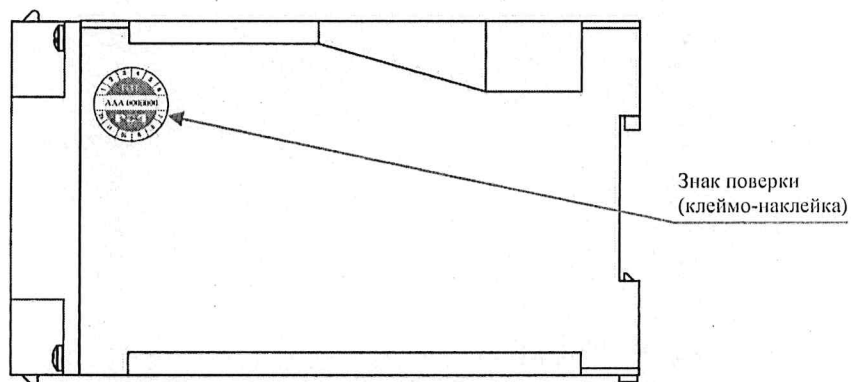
Схема с указанием места для нанесения знака поверки на преобразователи в корпусах МВ16
